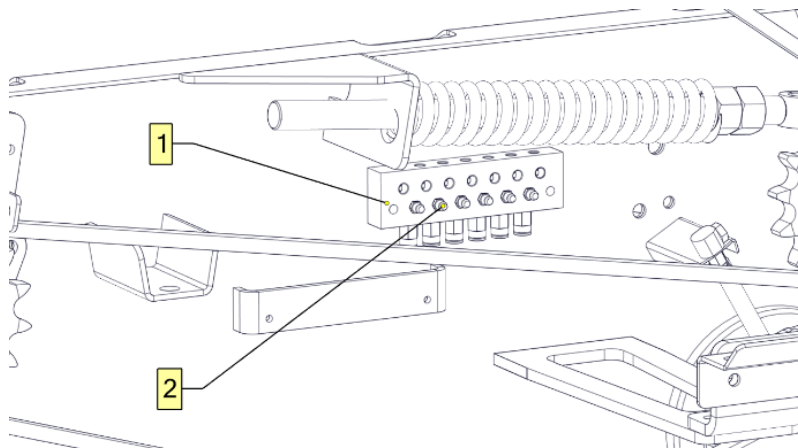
Центральная система смазки подшипников на левой стороне пресс-подборщика
